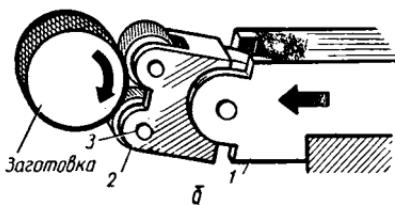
Притирка наружной цилиндрической поверхности на токарном станке:
